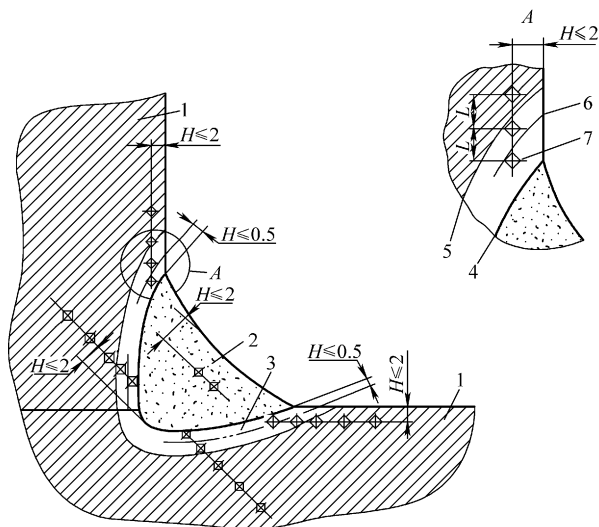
钢（奥氏体钢除外）角焊缝的测点位置
